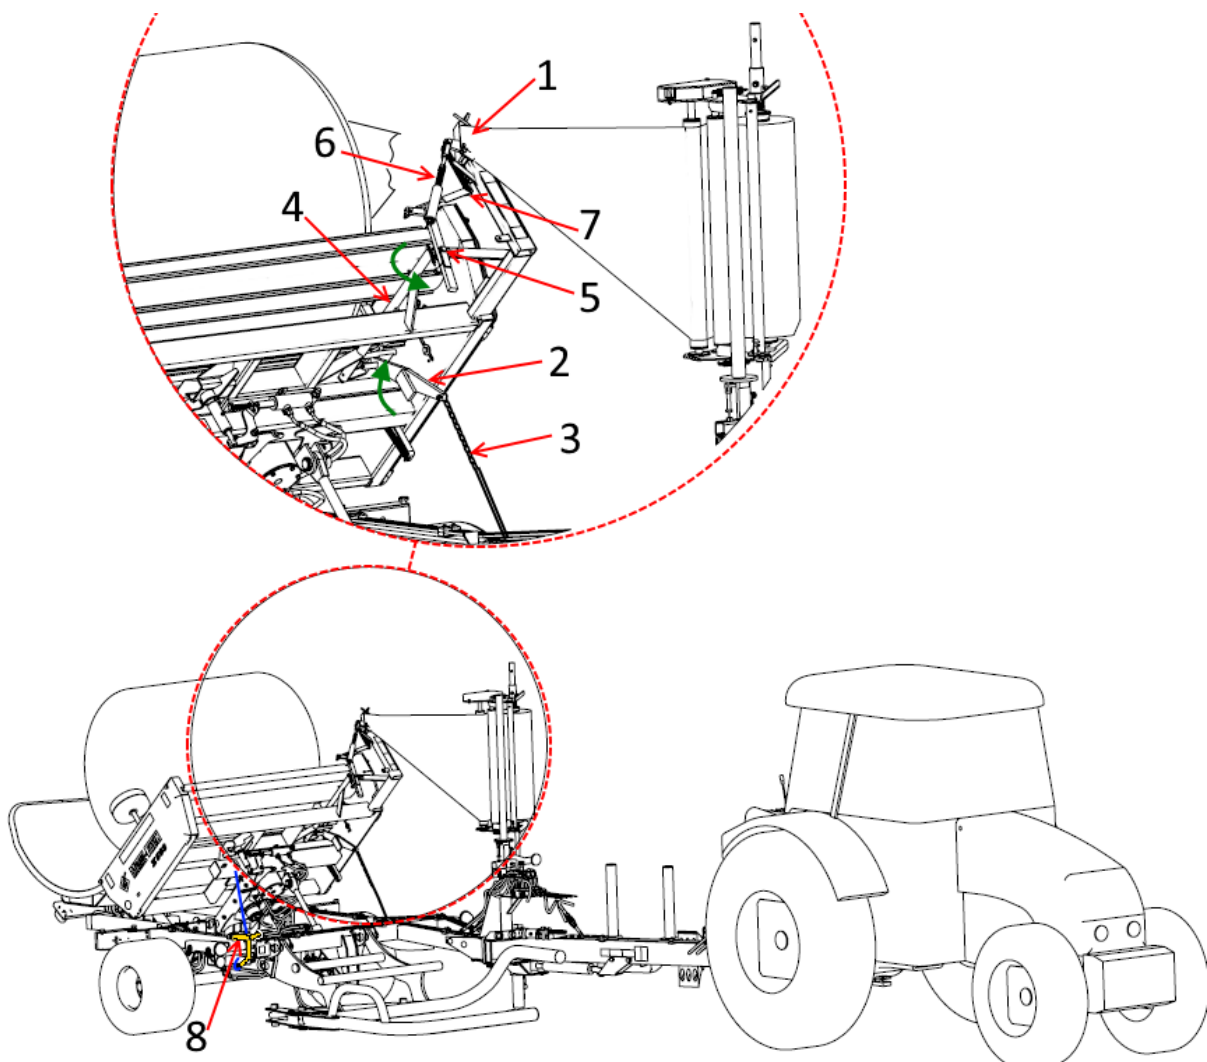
Ustawienie stołu roboczego i stawiacza bel do pozycji roboczej
